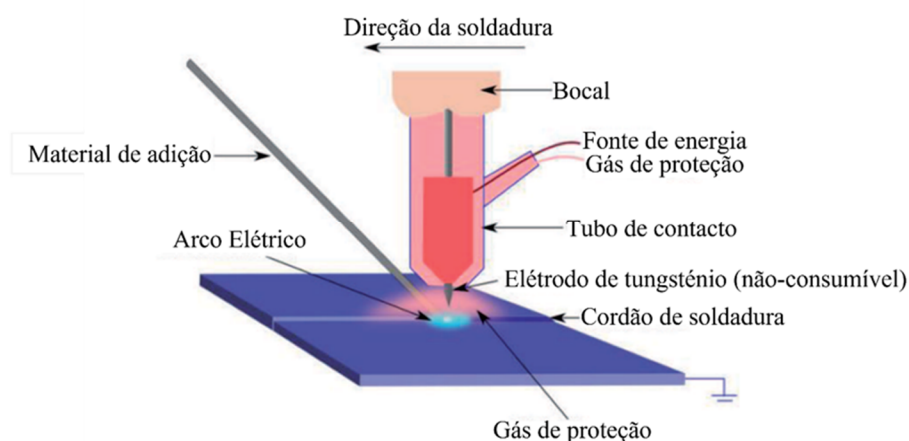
Esquema representativo da soldadura TIG (adaptado de [53])
